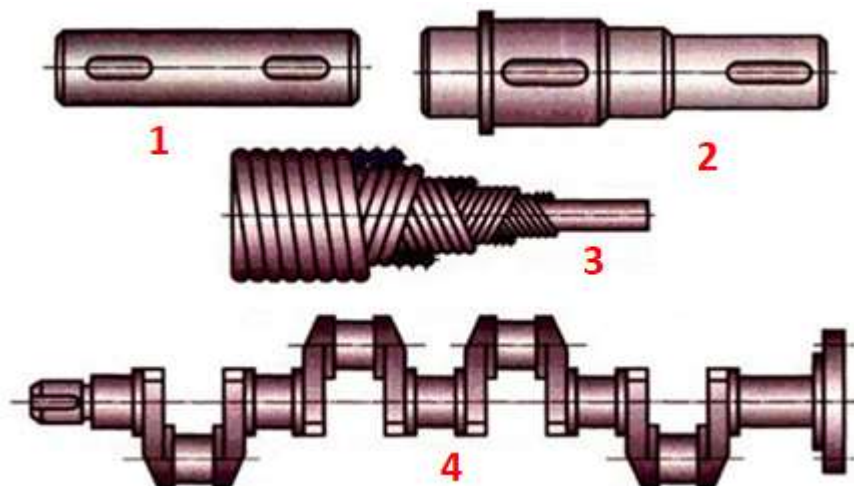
Основные типы валов и осей: 1 – гладкий, 2 – ступенчатый, 3 – гибкий, 4 - коленчатый
